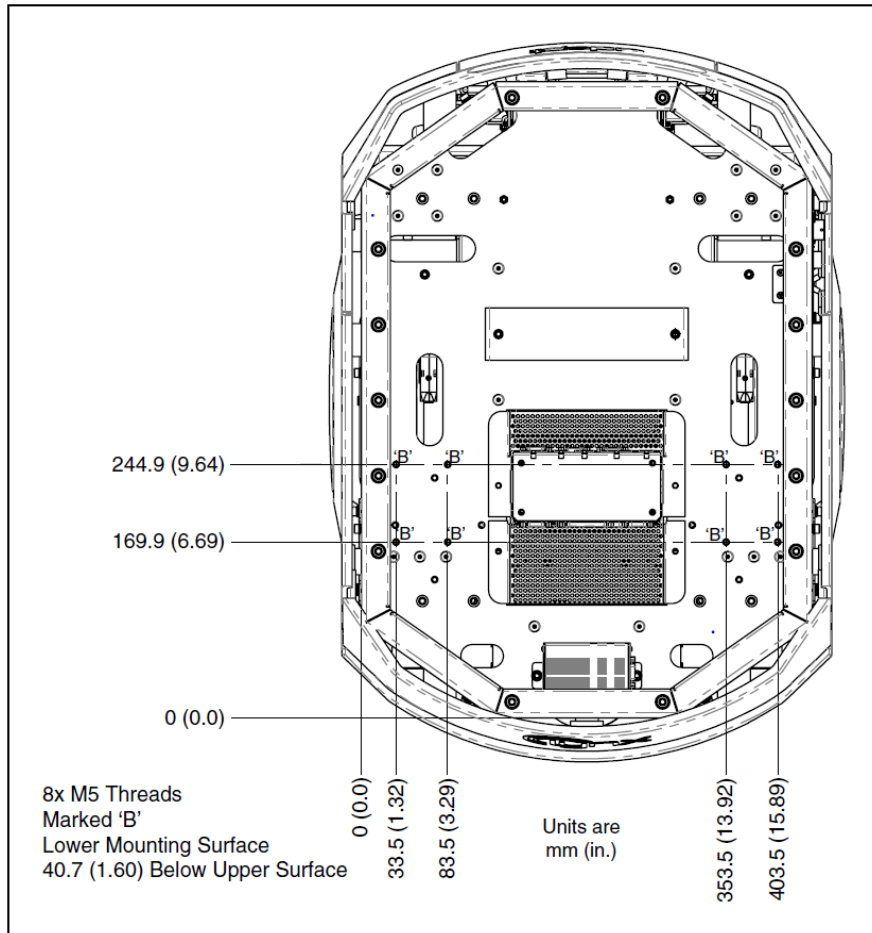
Dimensions du plateau de la plate-forme, pour la fixation de la structure de charge utile à l'aide de boulons à filetage M5
